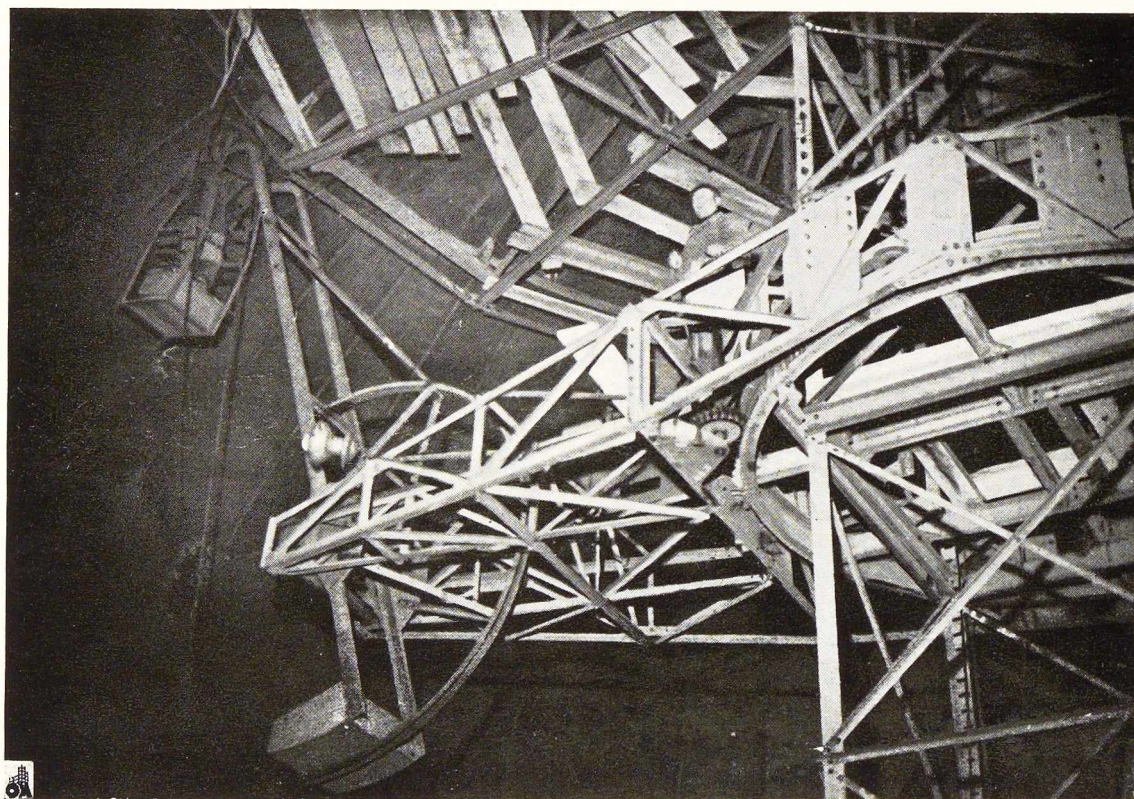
Le manège, pendant l'exécution des dernières soudures.
